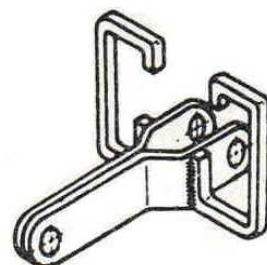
Řetěz svislého redleru s přerušenými unášeci; a) plastový unášec
